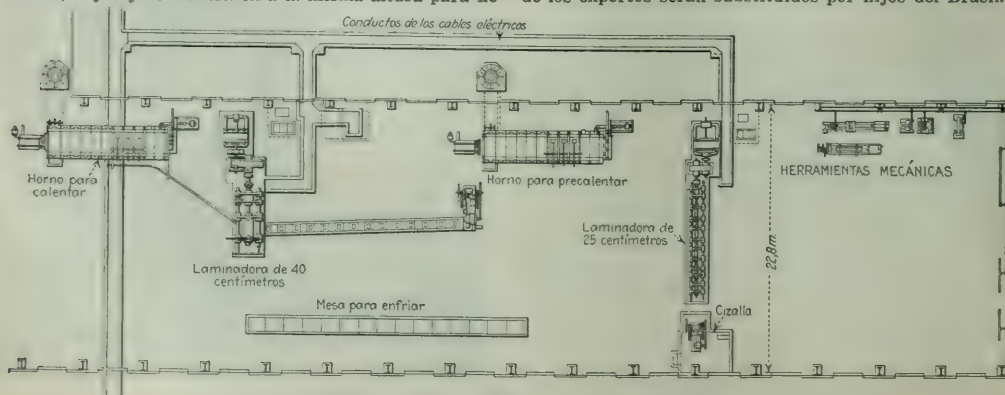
PLANO DE LA PLANTA DE LAMINADORAS
